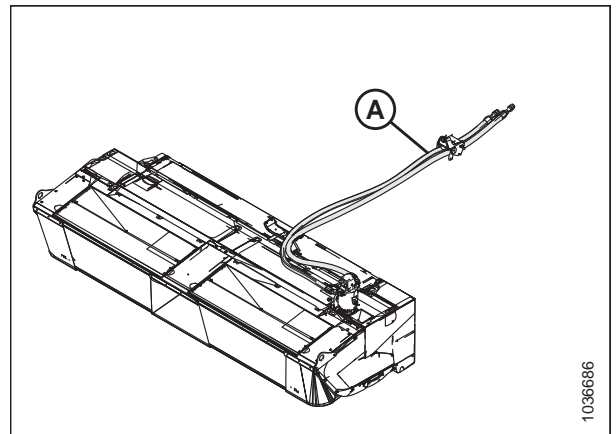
Напорные и обратные шланги – R113 SP
